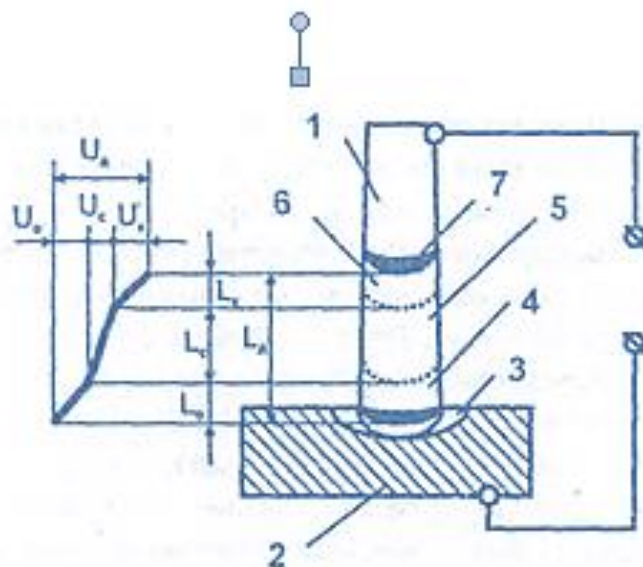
Схема сварочной дуги и падения напряжений в ней:
